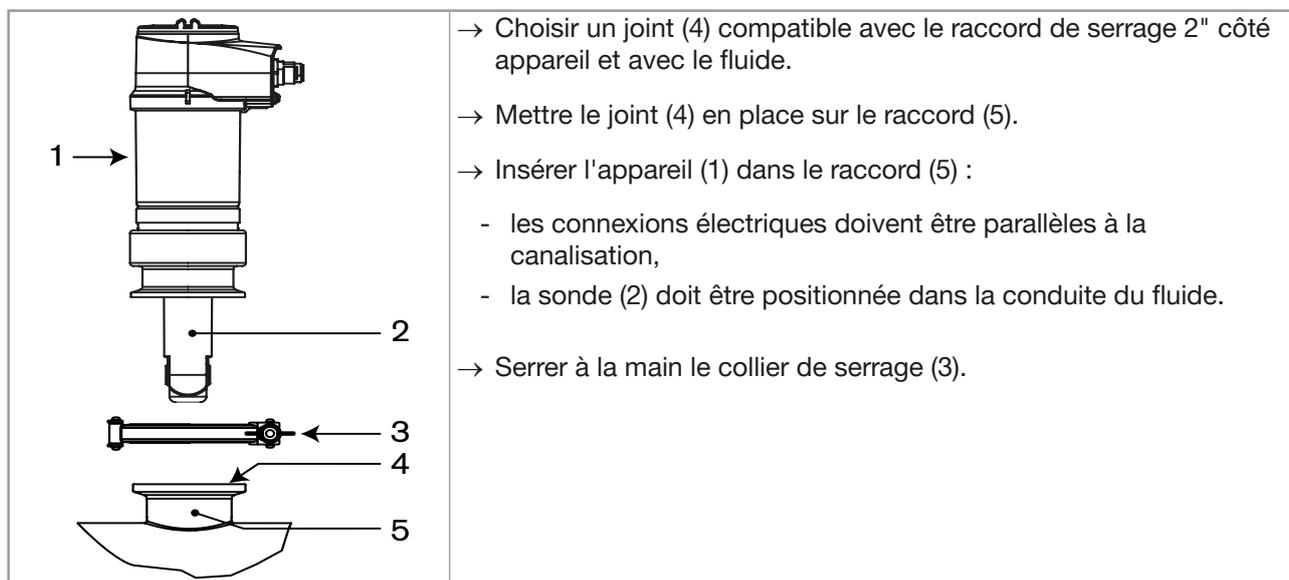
Installation d'une variante d'appareil avec raccord de serrage 2" sur la canalisation
